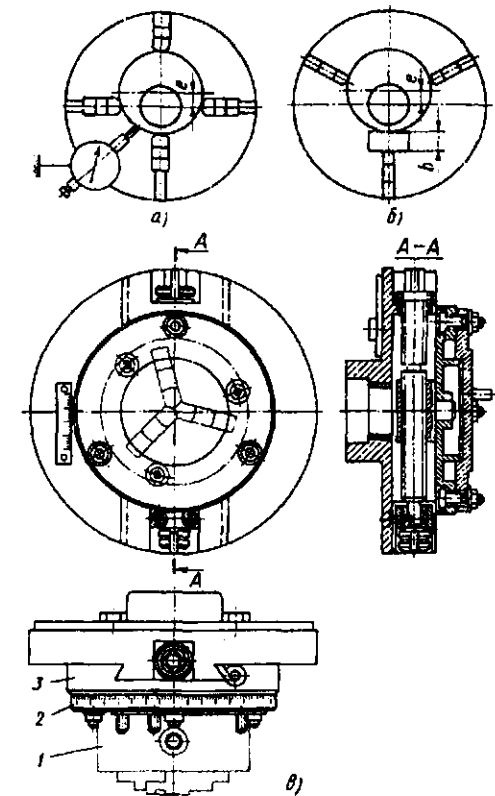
Схема обработки эксцентрических поверхностей заготовок при установке их в патроне со смещением
